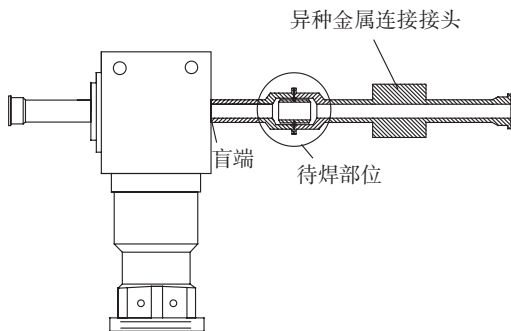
气动阀门与异种金属连接接头焊接结构示意图
